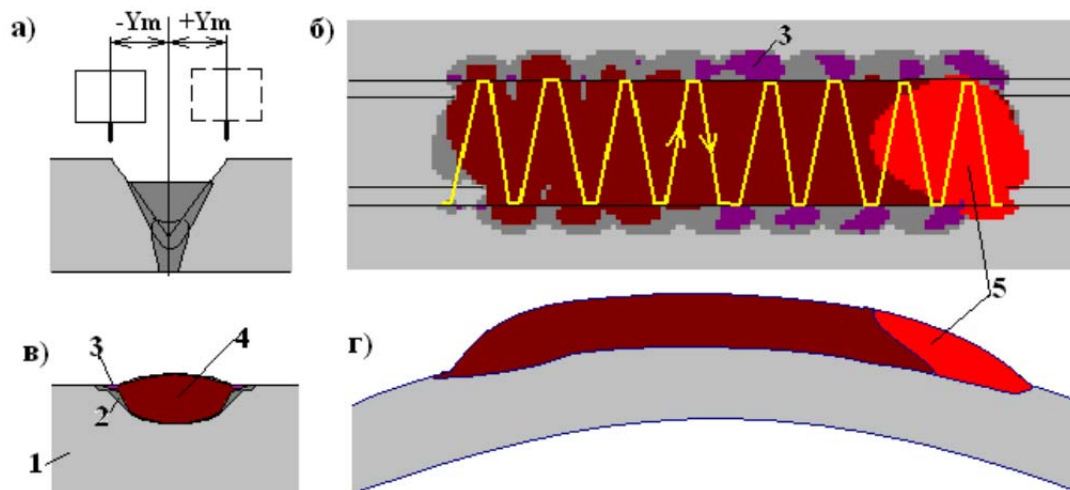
Формирование сварочной ванны и шва при сварке с поперечными колебаниями: а – сечение шва перед началом сварки; б – вид на стык сверху; в – сечение шва; г – сечение по плоскости симметрии стыка; 1 – исходный металл; 2 – зона периодического проплавления; 3 – зона периодического удаления расплавленного металла в сварочную ванну; 4 – зона устойчивого проплавления; 5 – сварочная ванна [4]
